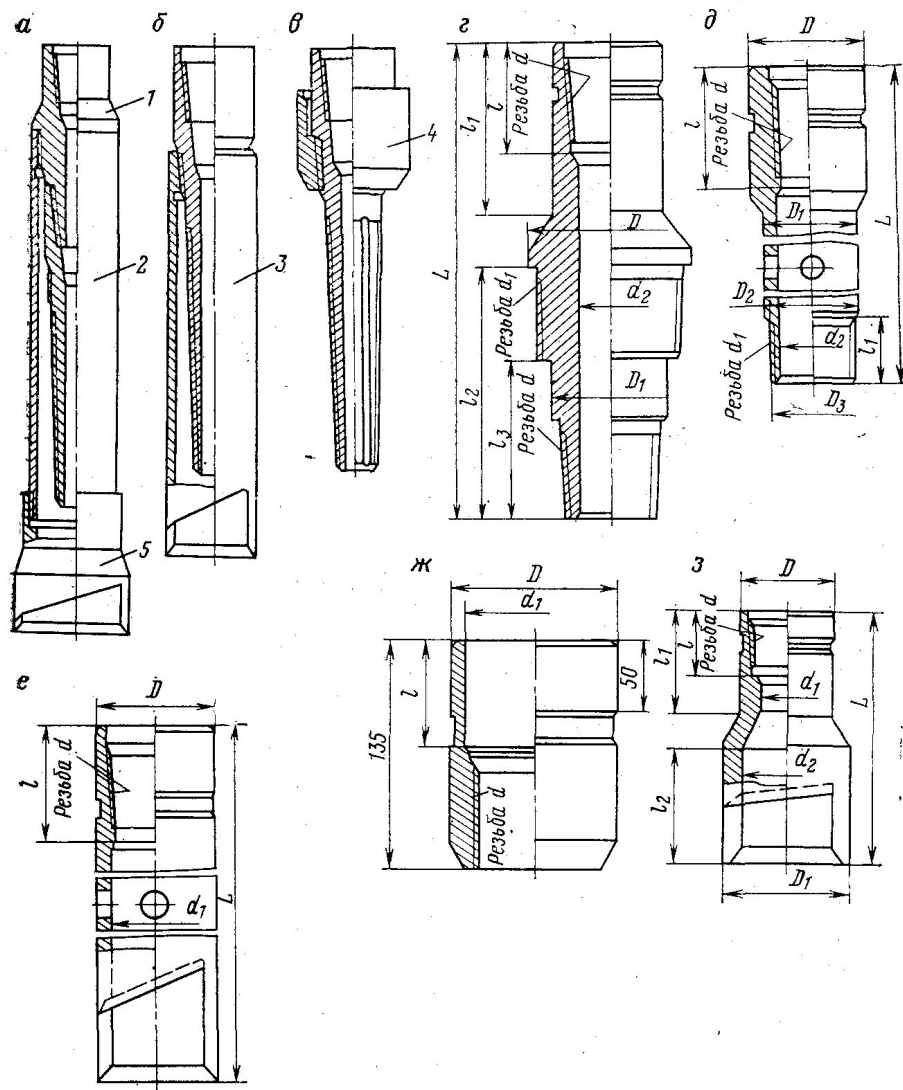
Центрирующие приспособления к ловильному инструменту:
